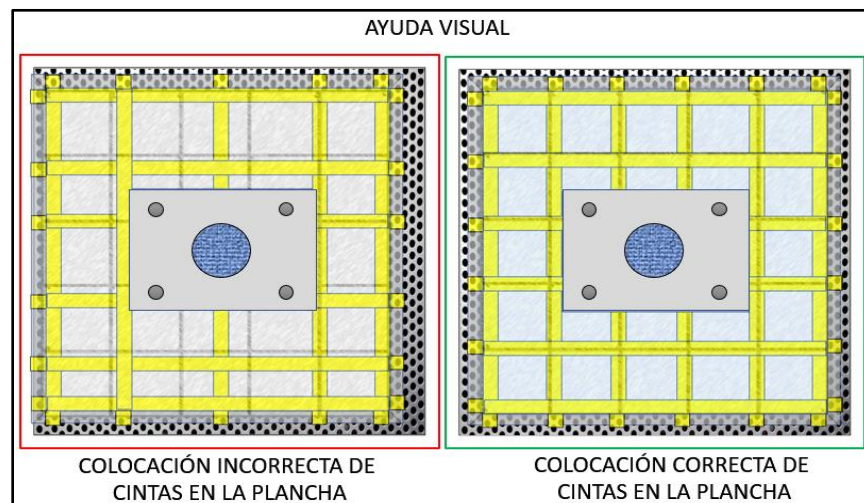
Ayuda visual, colocación de cintas en plancha de aspiración. Fuente: Elaboración propia.
